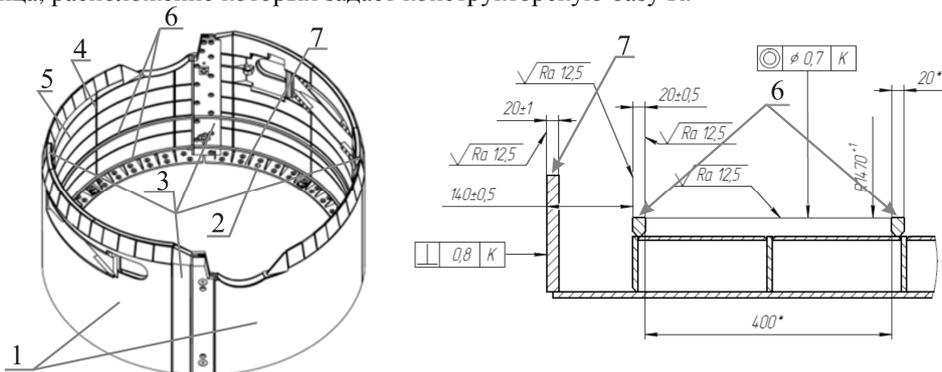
Общий вид головной секции геохода (1 – обечайки; 2 – фланцы; 3 – замки; 4 – стрингеры; 5 – шпангоуты; 6 – дорожки качения; 7 – внутренняя поверхность соединительного фланца)
